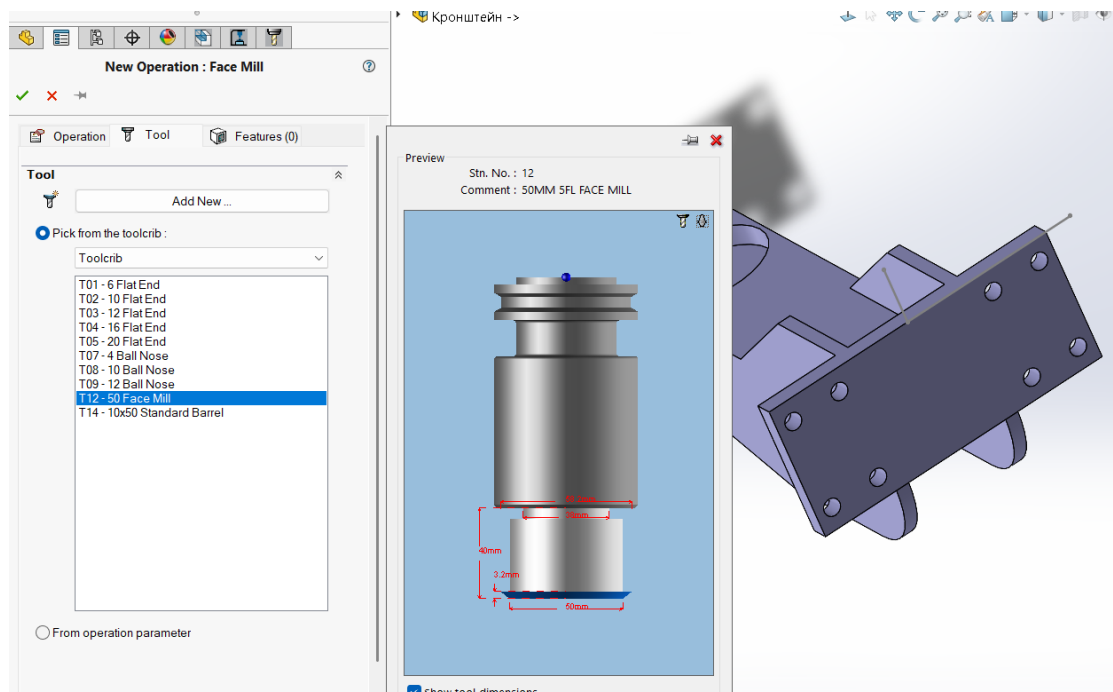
Face Mill з вибором інструменту для торцевого фрезерування горизонтальних поверхонь кронштейна
